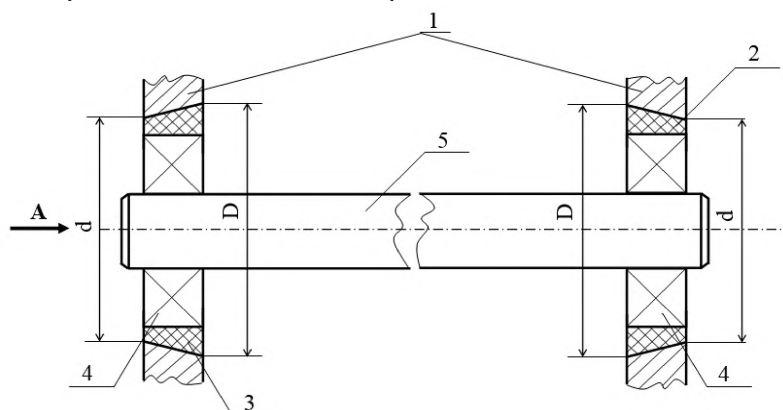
Схема установки вала на опорах с упругими усеченными коническими втулками
